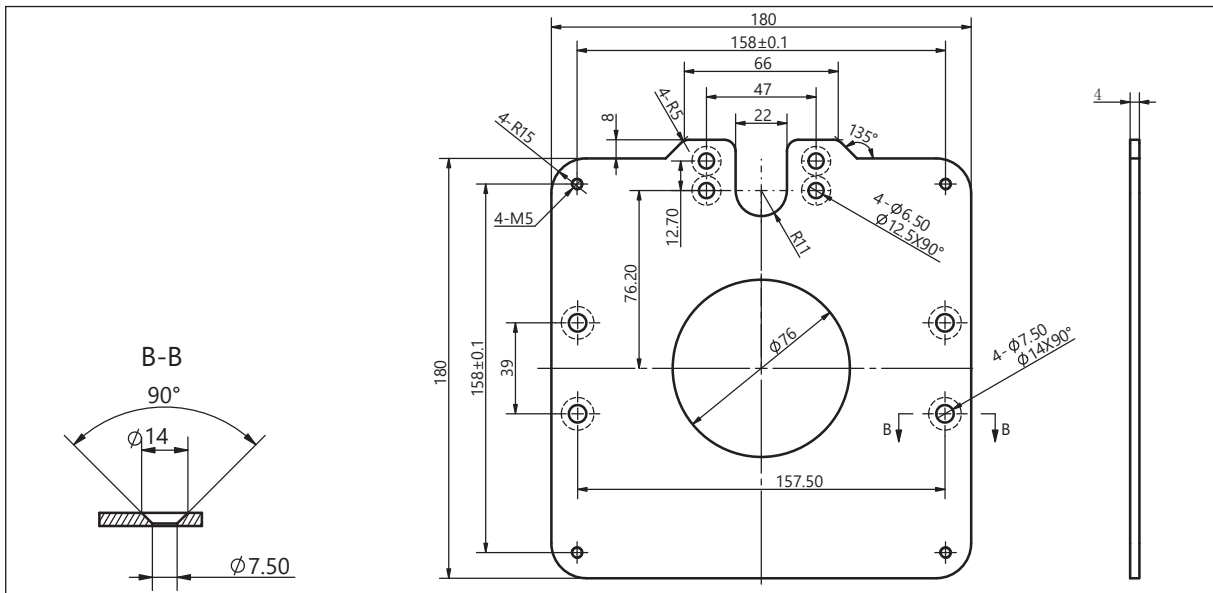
Пластина №2 – для установки фрезерного лифта BELMASH D033A.
